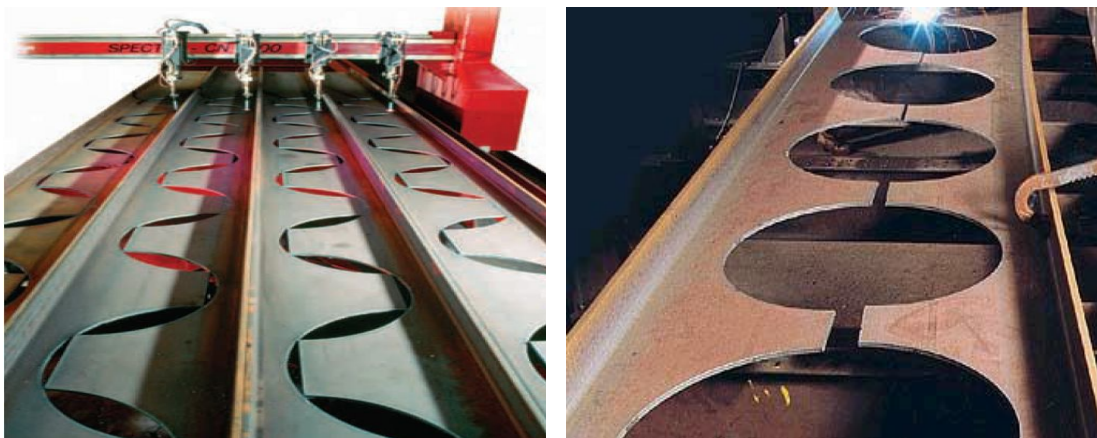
Fabricação de viga celular: corte com máquinas CNC e soldagem (WESTOK, 2012).
